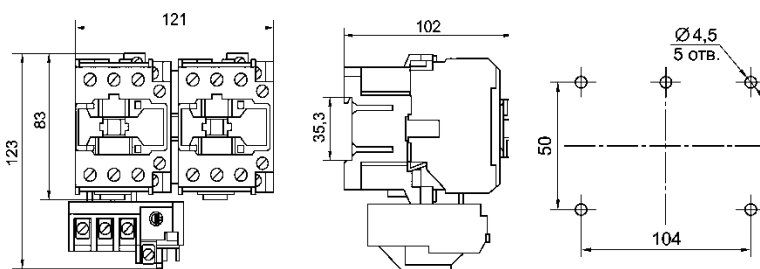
Пускатель реверсивный ПМ12-040 40А.
